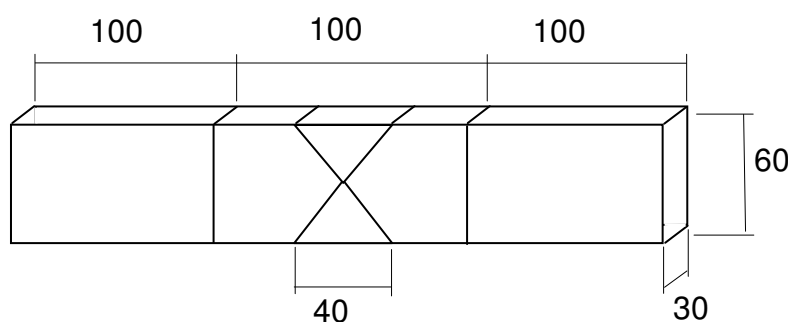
Esquema da divisão da junta soldada para obtenção dos corpos-de-prova – dimensões em mm.
